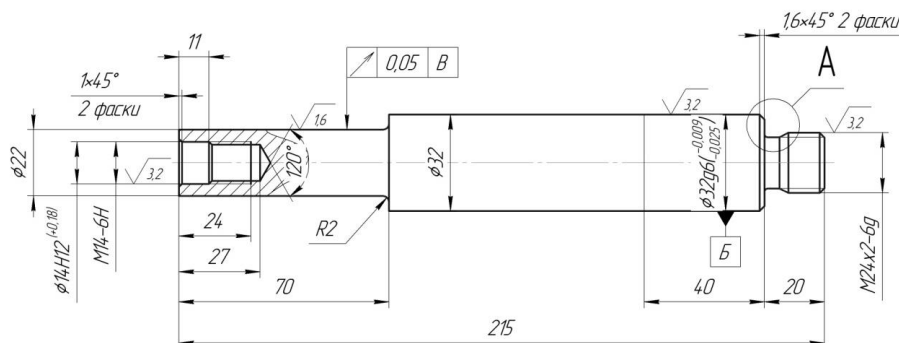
Оправочный стержень для крепления оправки прошивного стана
